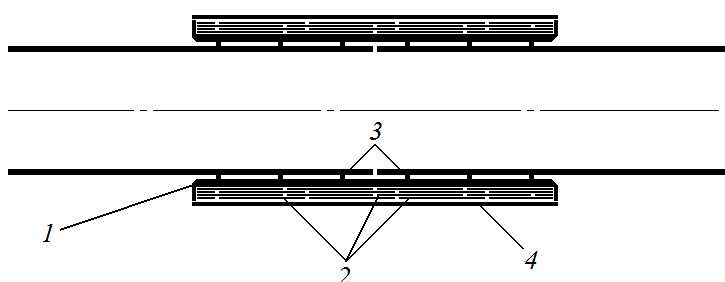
Сборная соединительная муфта с ЭПФ. 1 - соединительный трубчатый корпус (катушка); 2 – лентовидный РЭП из содержащего ниобий никелида титана; 3 – стыкуемые трубы; 4 – защитный пластиковый кожух
